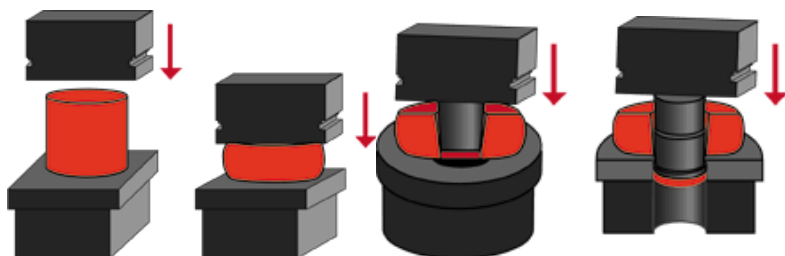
Обработка заготовки на 3-позиционном прессе
